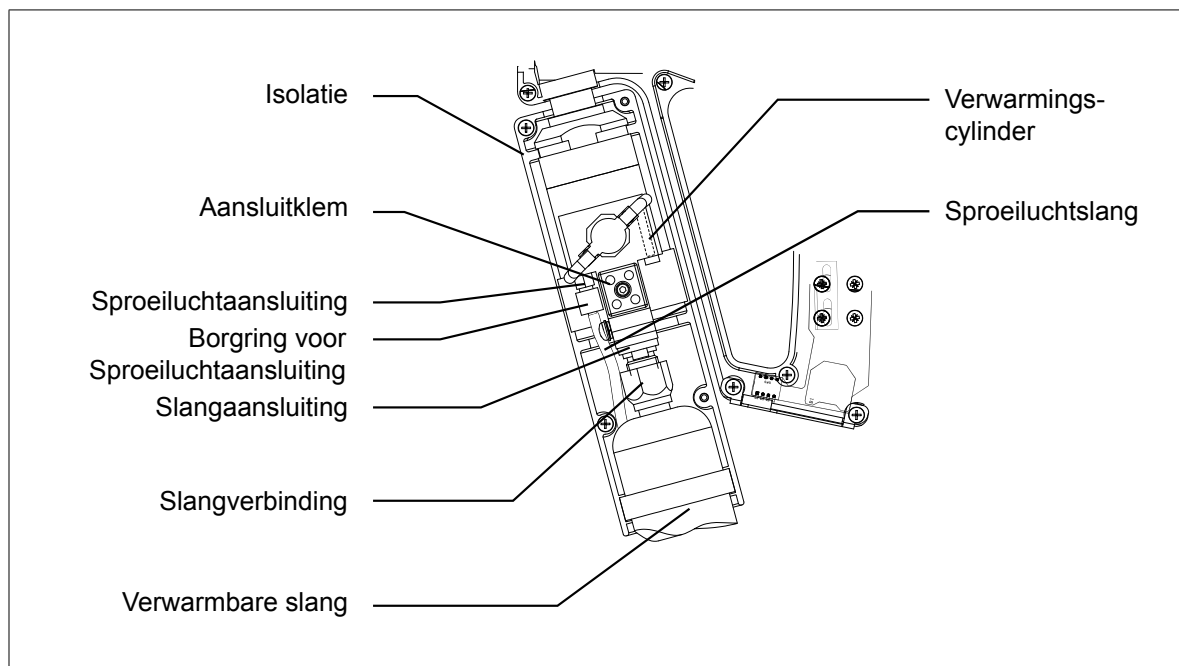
/1: Slangaansluiting in detail (voorbeeld van de HS-versie)
